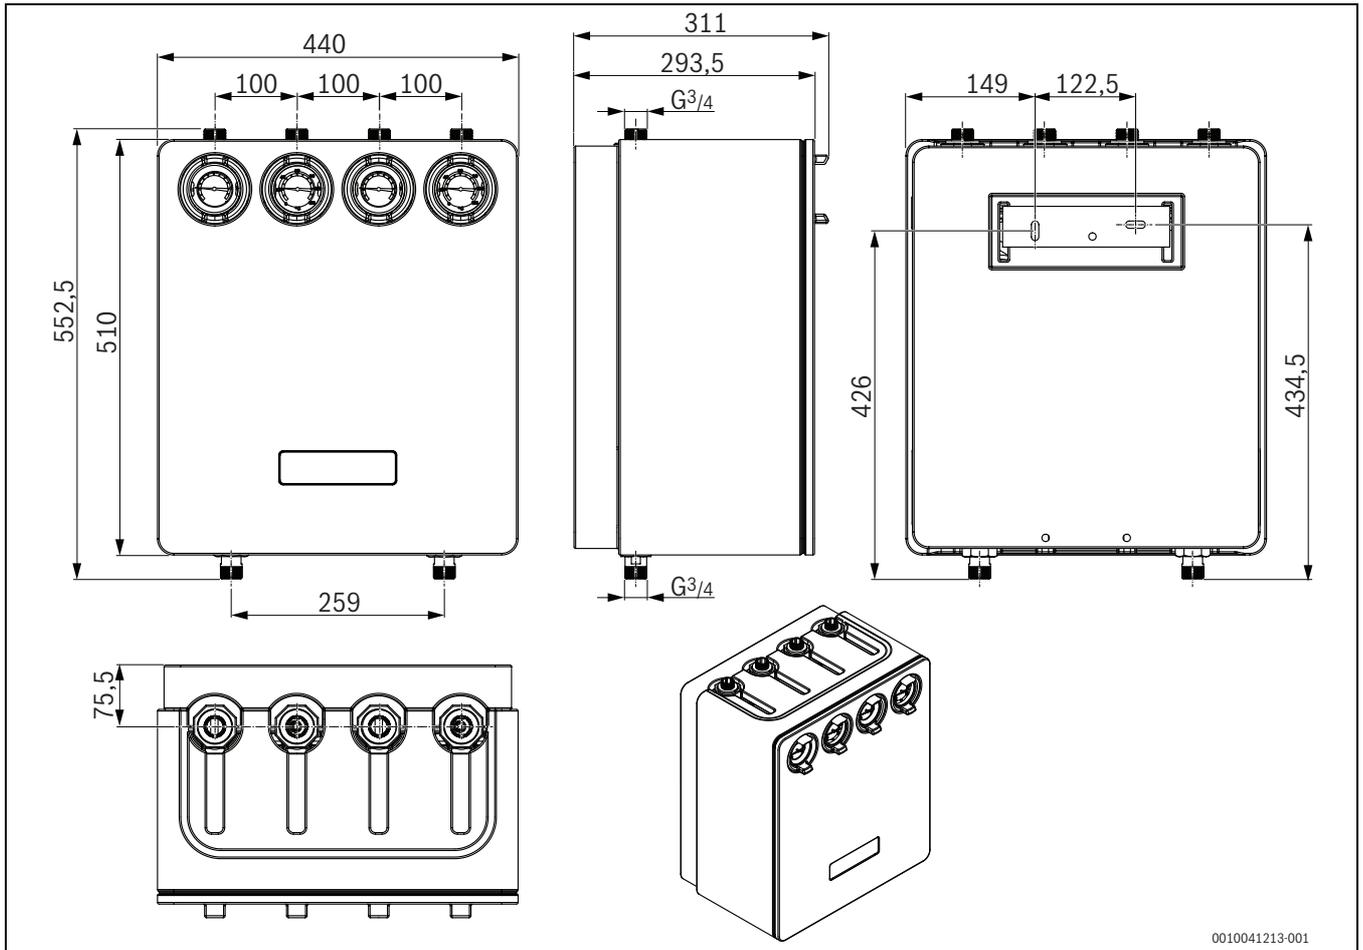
Abmessungen und Anschlüsse (Maße in mm)
